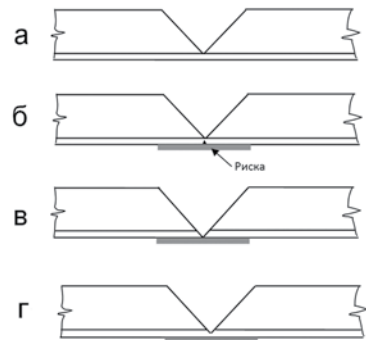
Расположение вершины паза при обработке деталей, облицованных разными материалами: а – эластичными термопластичными пленками из пластмасс; б – неэластичными (стекловидными) лаковыми покрытиями или термореактивным пластиком; в – натуральным шпоном при поперечном направлении его волокон по отношению к пазу; г – натуральным шпоном при продольном направлении его волокон по отношению к пазу
